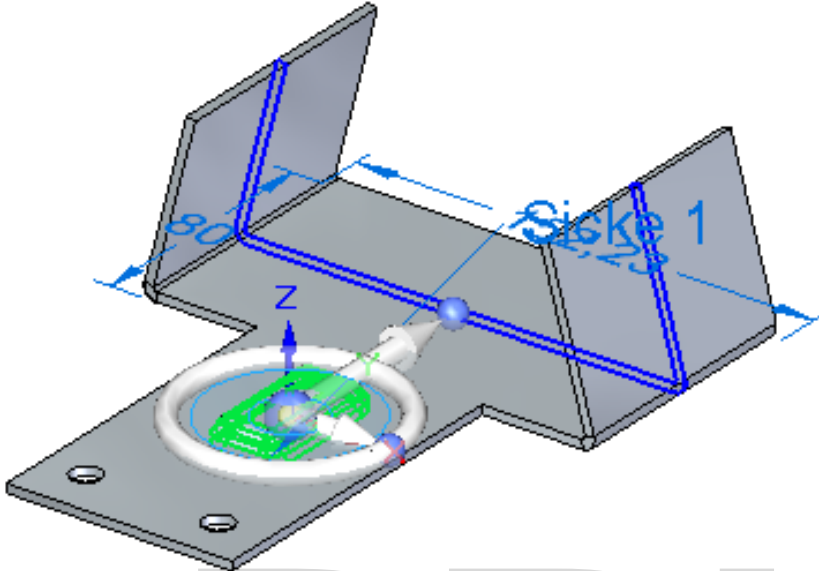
2D-Steuerrad für die Bearbeitung von Sicken und anderen prozessorientierten Formelementen
